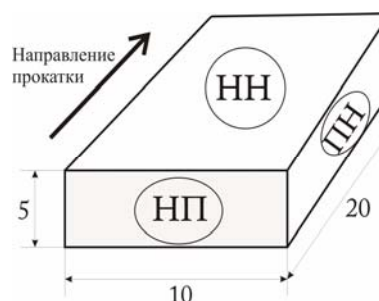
Эскиз образца с обозначенными плоскостями относительно направления прокатки
